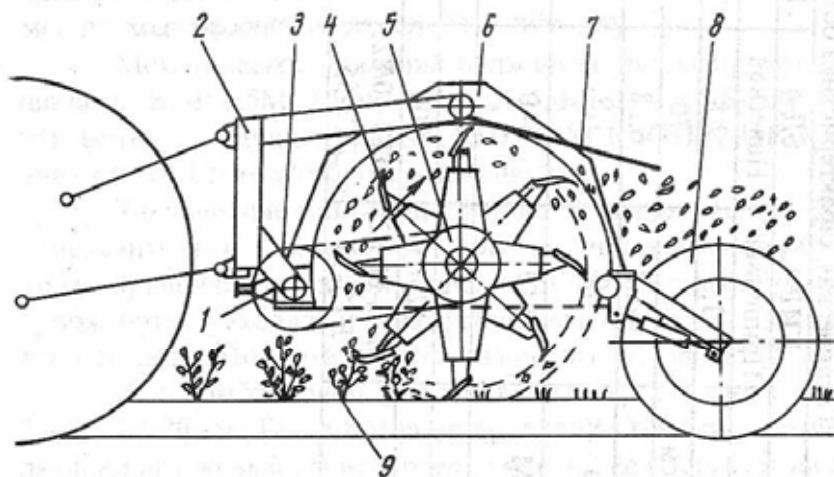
Технологическая схема ботводробителя: 1 - редуктор; 2 - автосцепка; 3 - приводной шкив; 4 - нож; 5 - ротор; 6 - рама; 7 - кожух-направитель; 8 - опорное колесо; 9 - вершина гребня
